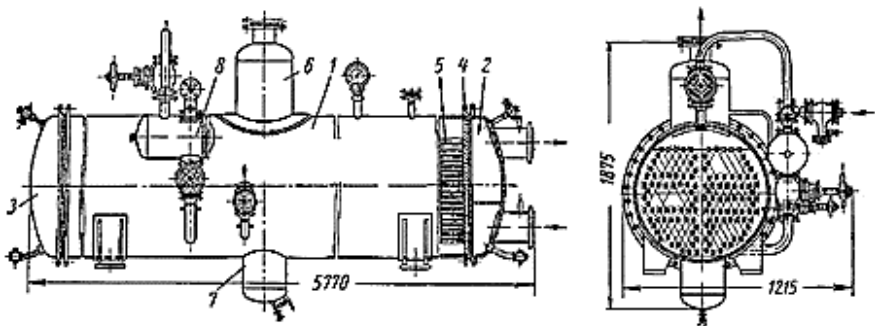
Аміачний кожухотрубний випарник: 1 – корпус, 2 і 3 – кришки; 4 – трубні ґрати; 5 – труби; 6 – сухопарник; 7 – відстійник, 8 – вентиль регулюючий
